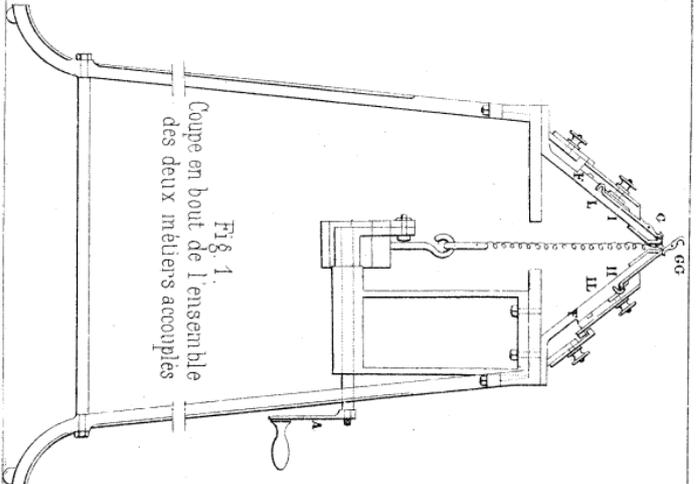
Coupe en bout de l'ensemble des deux métiers accouplés
